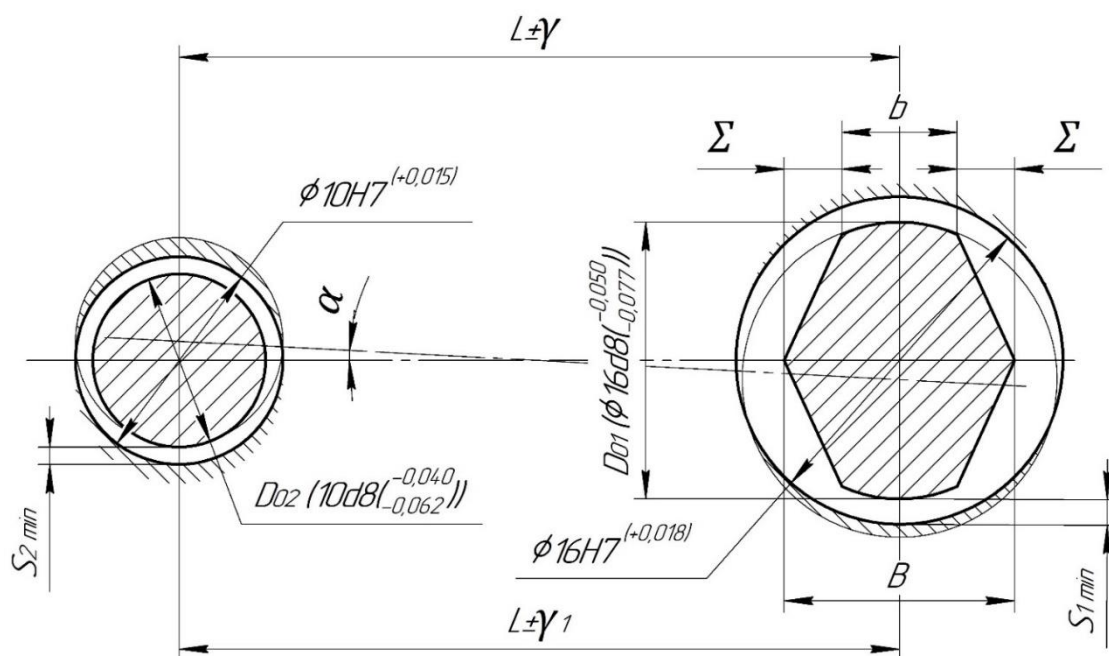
Схема установлення заготовки базовими отворами на циліндричний і зрізаний палець
